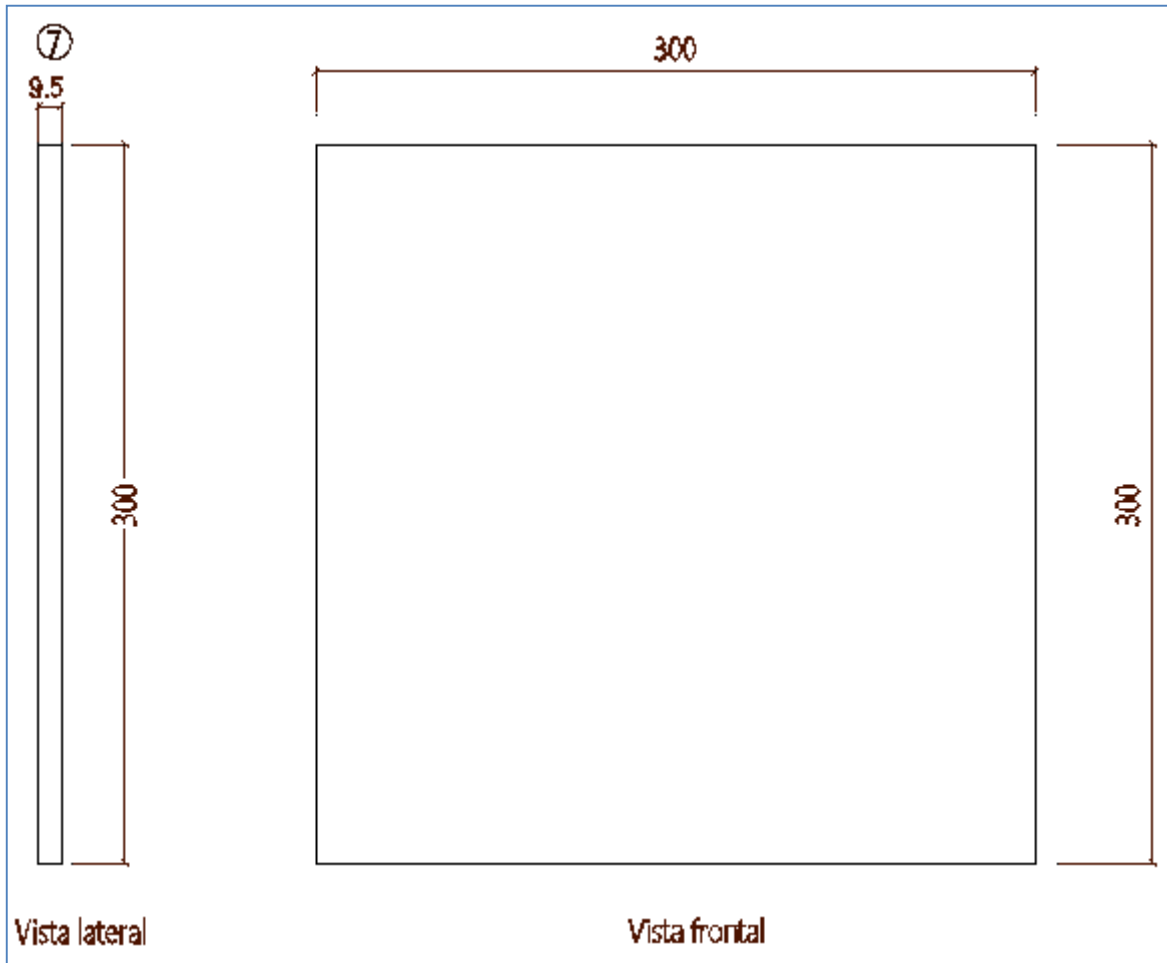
Detalle despiece pieza No.7 modelo 1 tensión.
